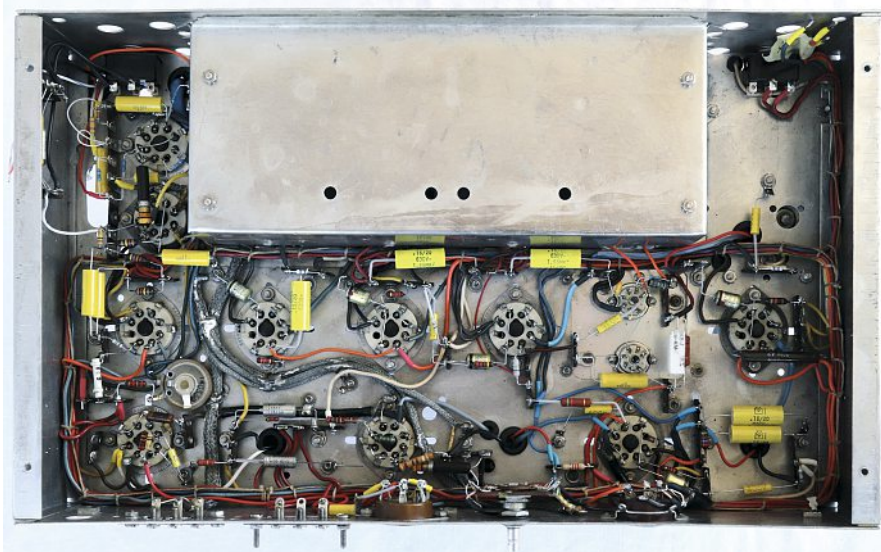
Chassis, erneuert, noch ohne Frontelemente
